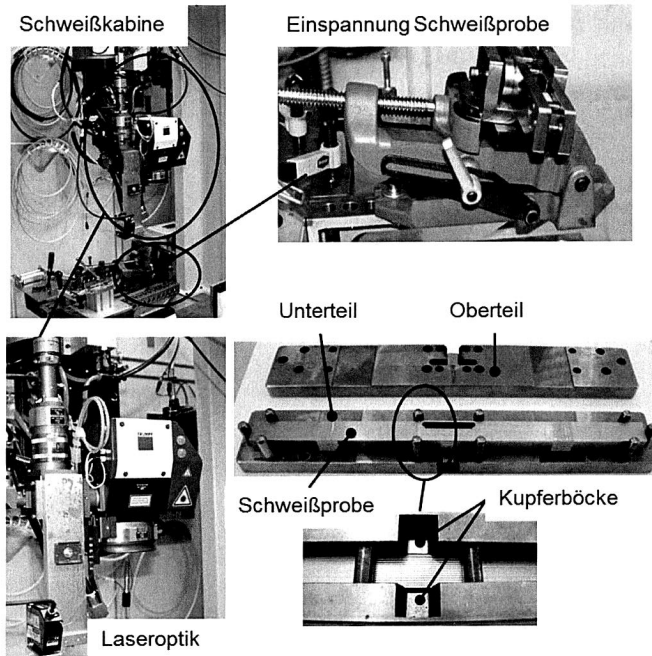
Schweißkabine, Laseroptik und Einspannung der Schweißproben.
